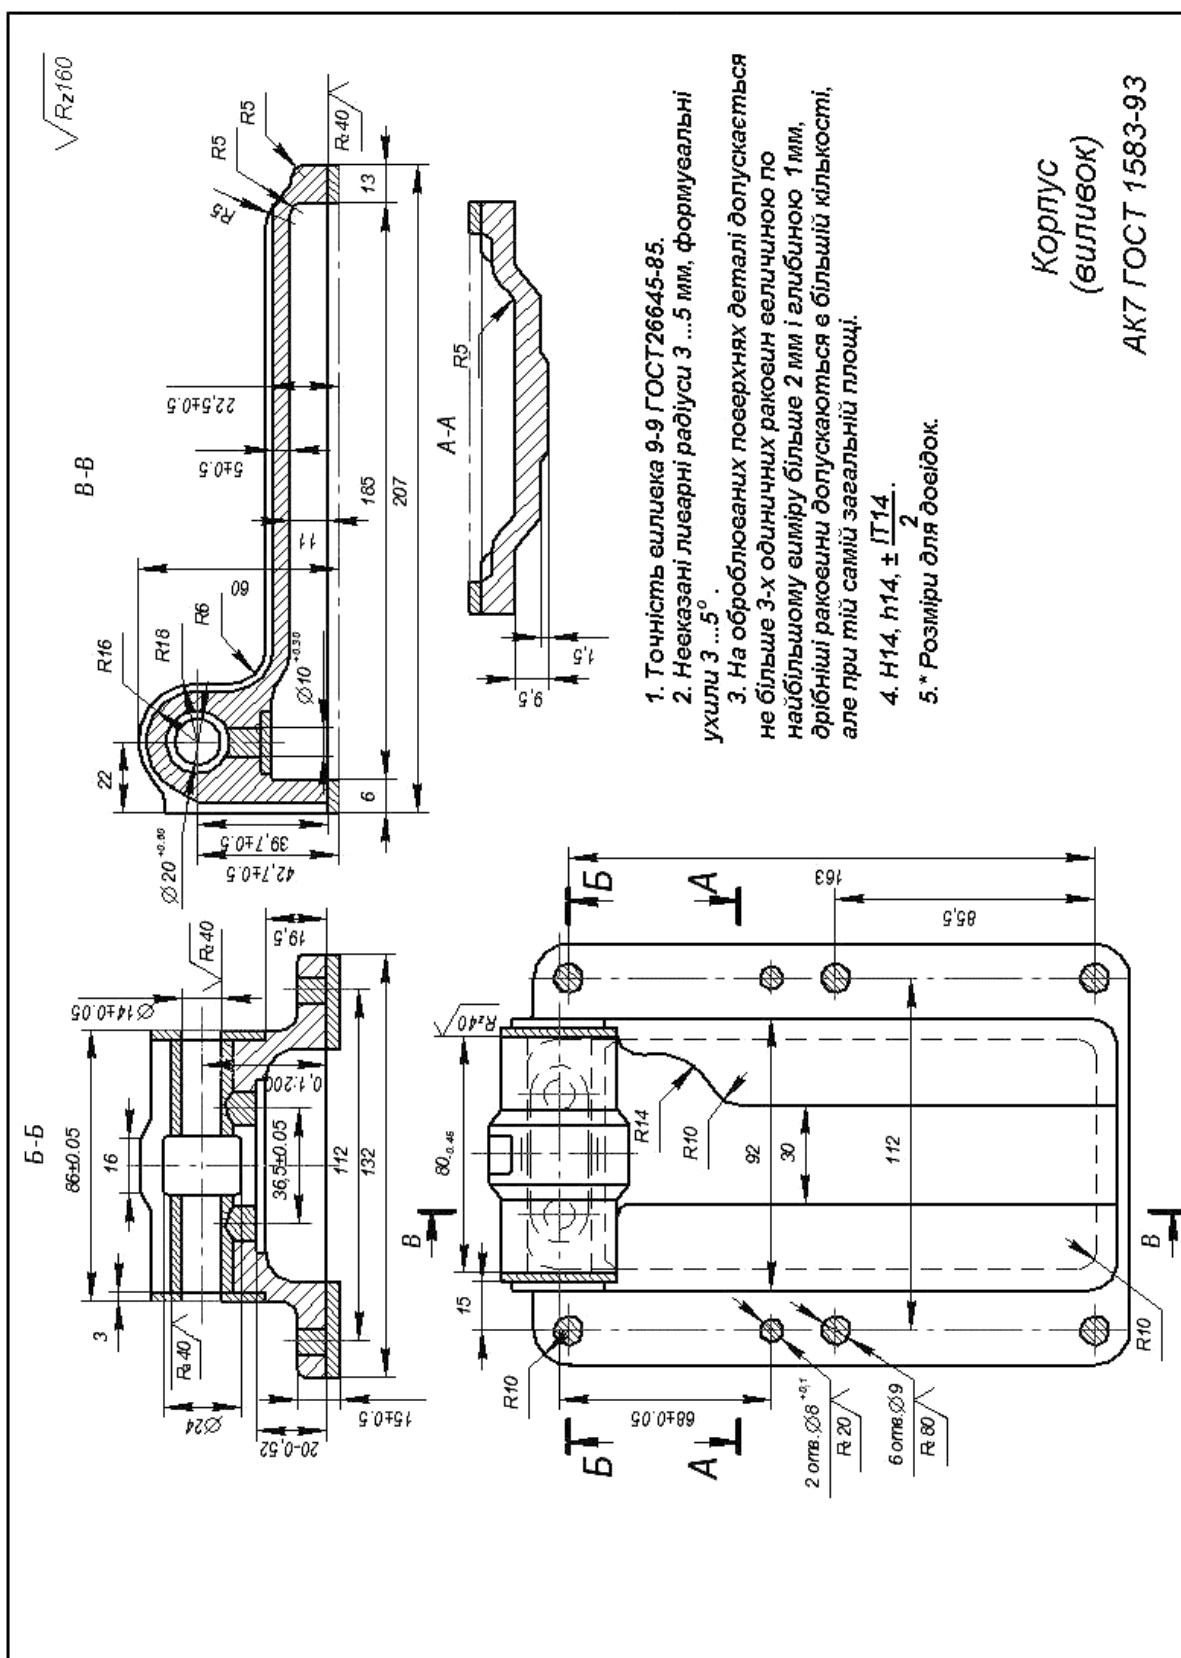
Заготовка корпуса, одержана методом литва
